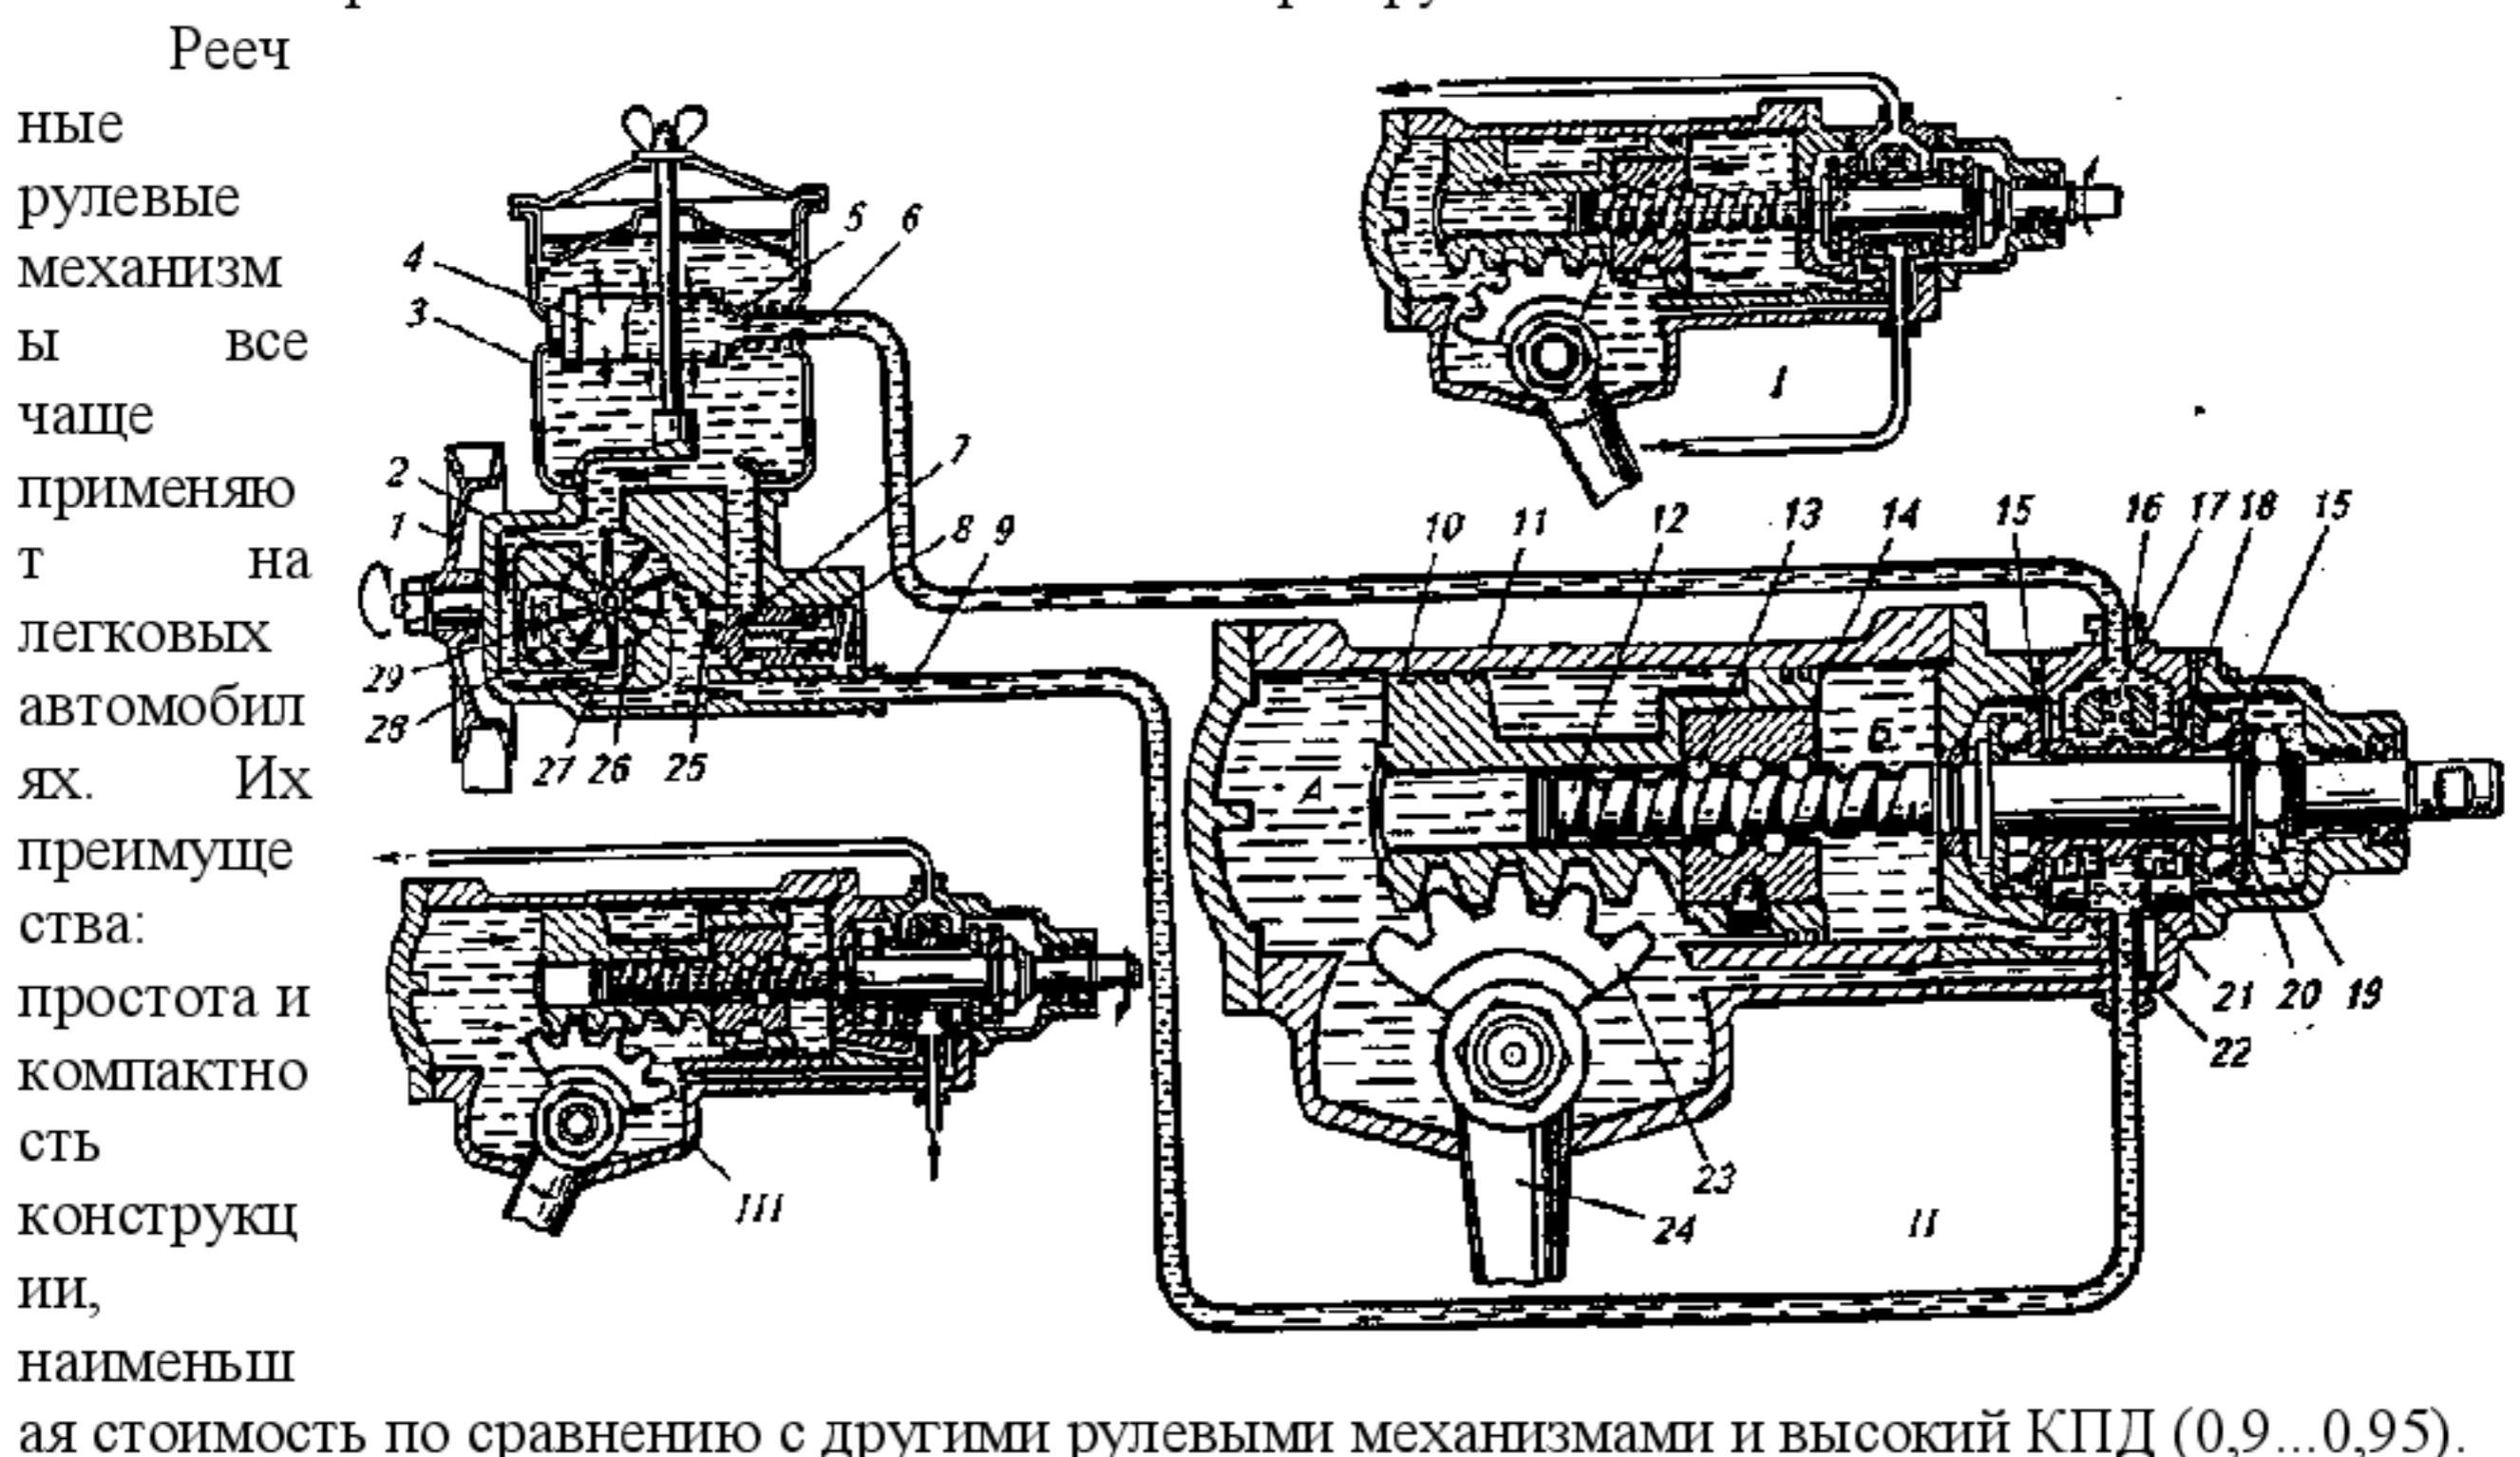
Рулевой механизм типа винт-гайка и рейка-сектор: I – поворот направо; II – нейтральное положение; III – поворот налево; 1 – шкив привода насоса; 2 – насос гидроусилителя; 3 – бачок насоса; 4 – фильтр; 5 – предохранительный клапан фильтра; 6 – линия слива; 7 – перепускной клапан; 8 – предохранительный клапан; 9 – трубопровод высокого давления; 10 – поршень-рейка; 11 – картер рулевого механизма; 12 – винт; 13 – шарик; 14 –
